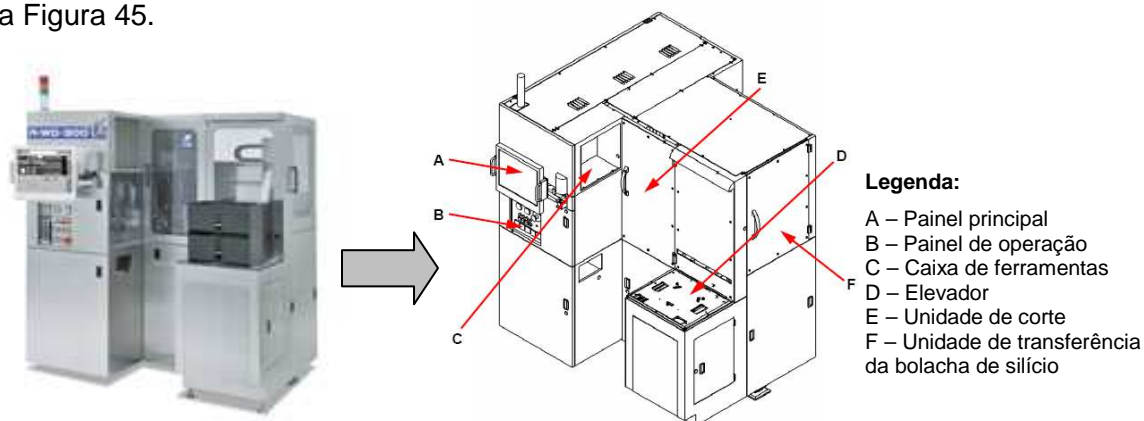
Imagem e partes constituintes do equipamento A-WD-300TX [12].
